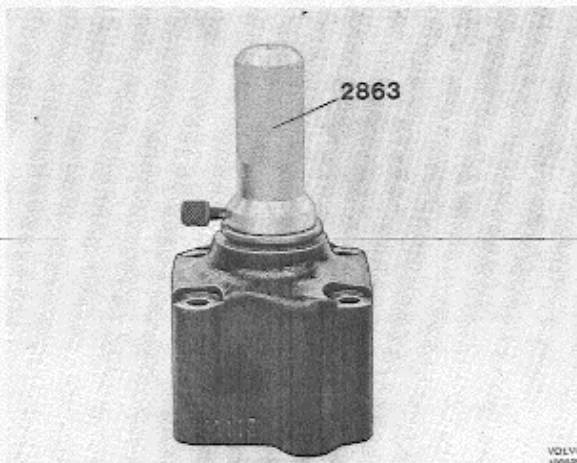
Einpressen des Wellendichtungsringes, Schneckenwelle
